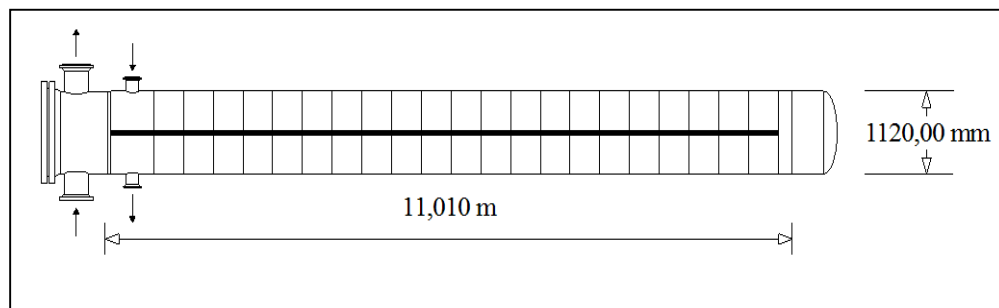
Dimensiones generales Recalentador. Fuente: HTRI Output drawing.
